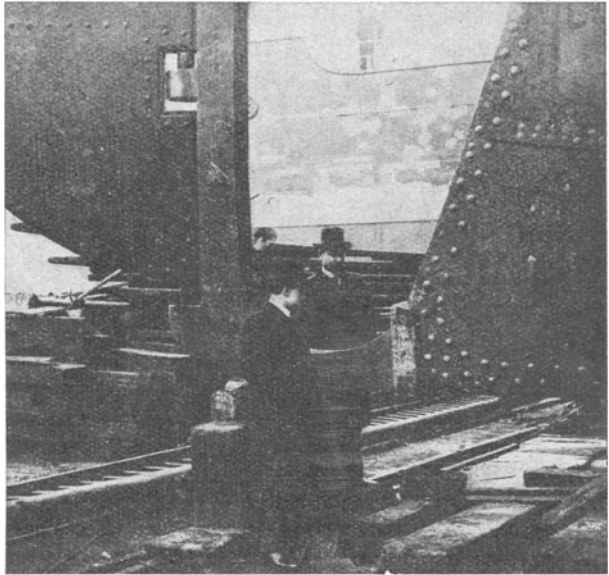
Schiffssteven, geschweißt mit Thermit.
